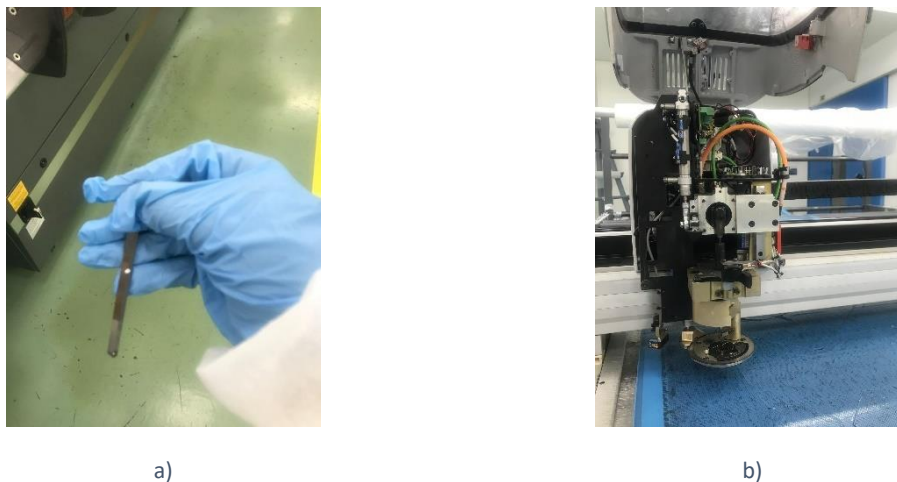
(a) Lâmina de corte e (b) Máquina de corte
